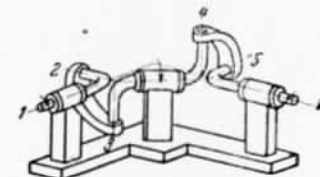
Пространственный шестизвенный шарнирный механизм.
